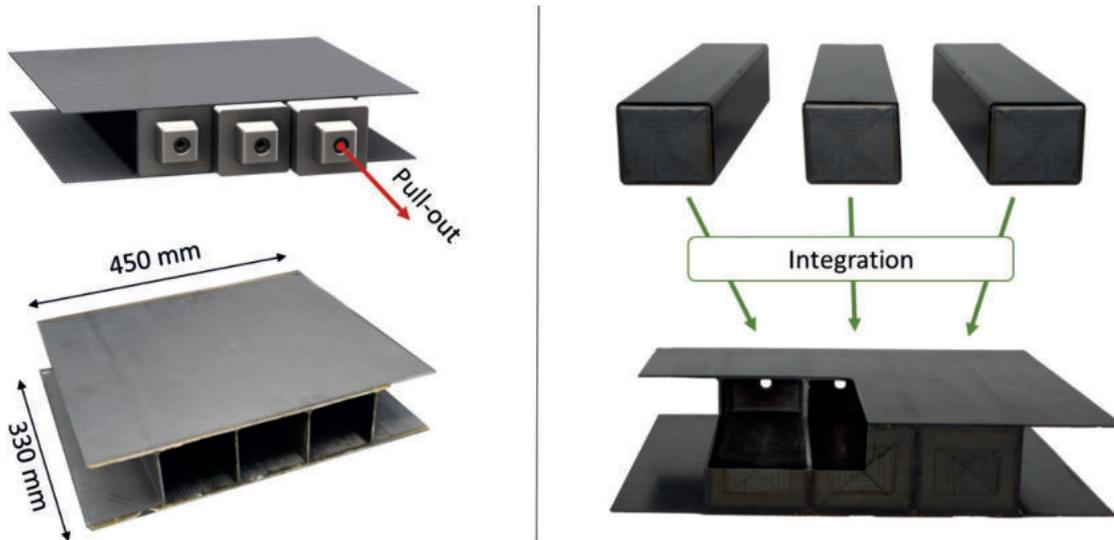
Demonstratorbauteil Multicell-Box: Referenzbauweise mit Kernauszugsverfahren (links) und neue Bauweise mit integrierten strukturellen Kernen (rechts, Schnittansicht)
